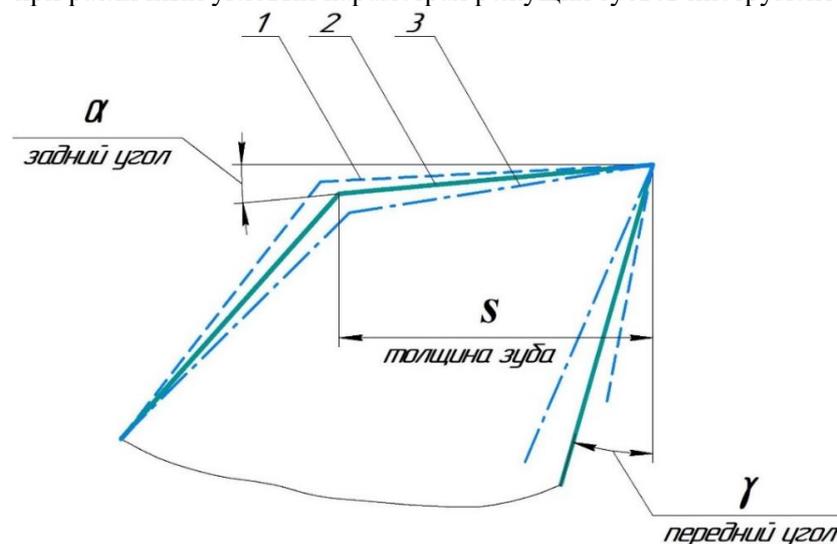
Эскиз режущего зуба прошивки при различных углах заточки:
